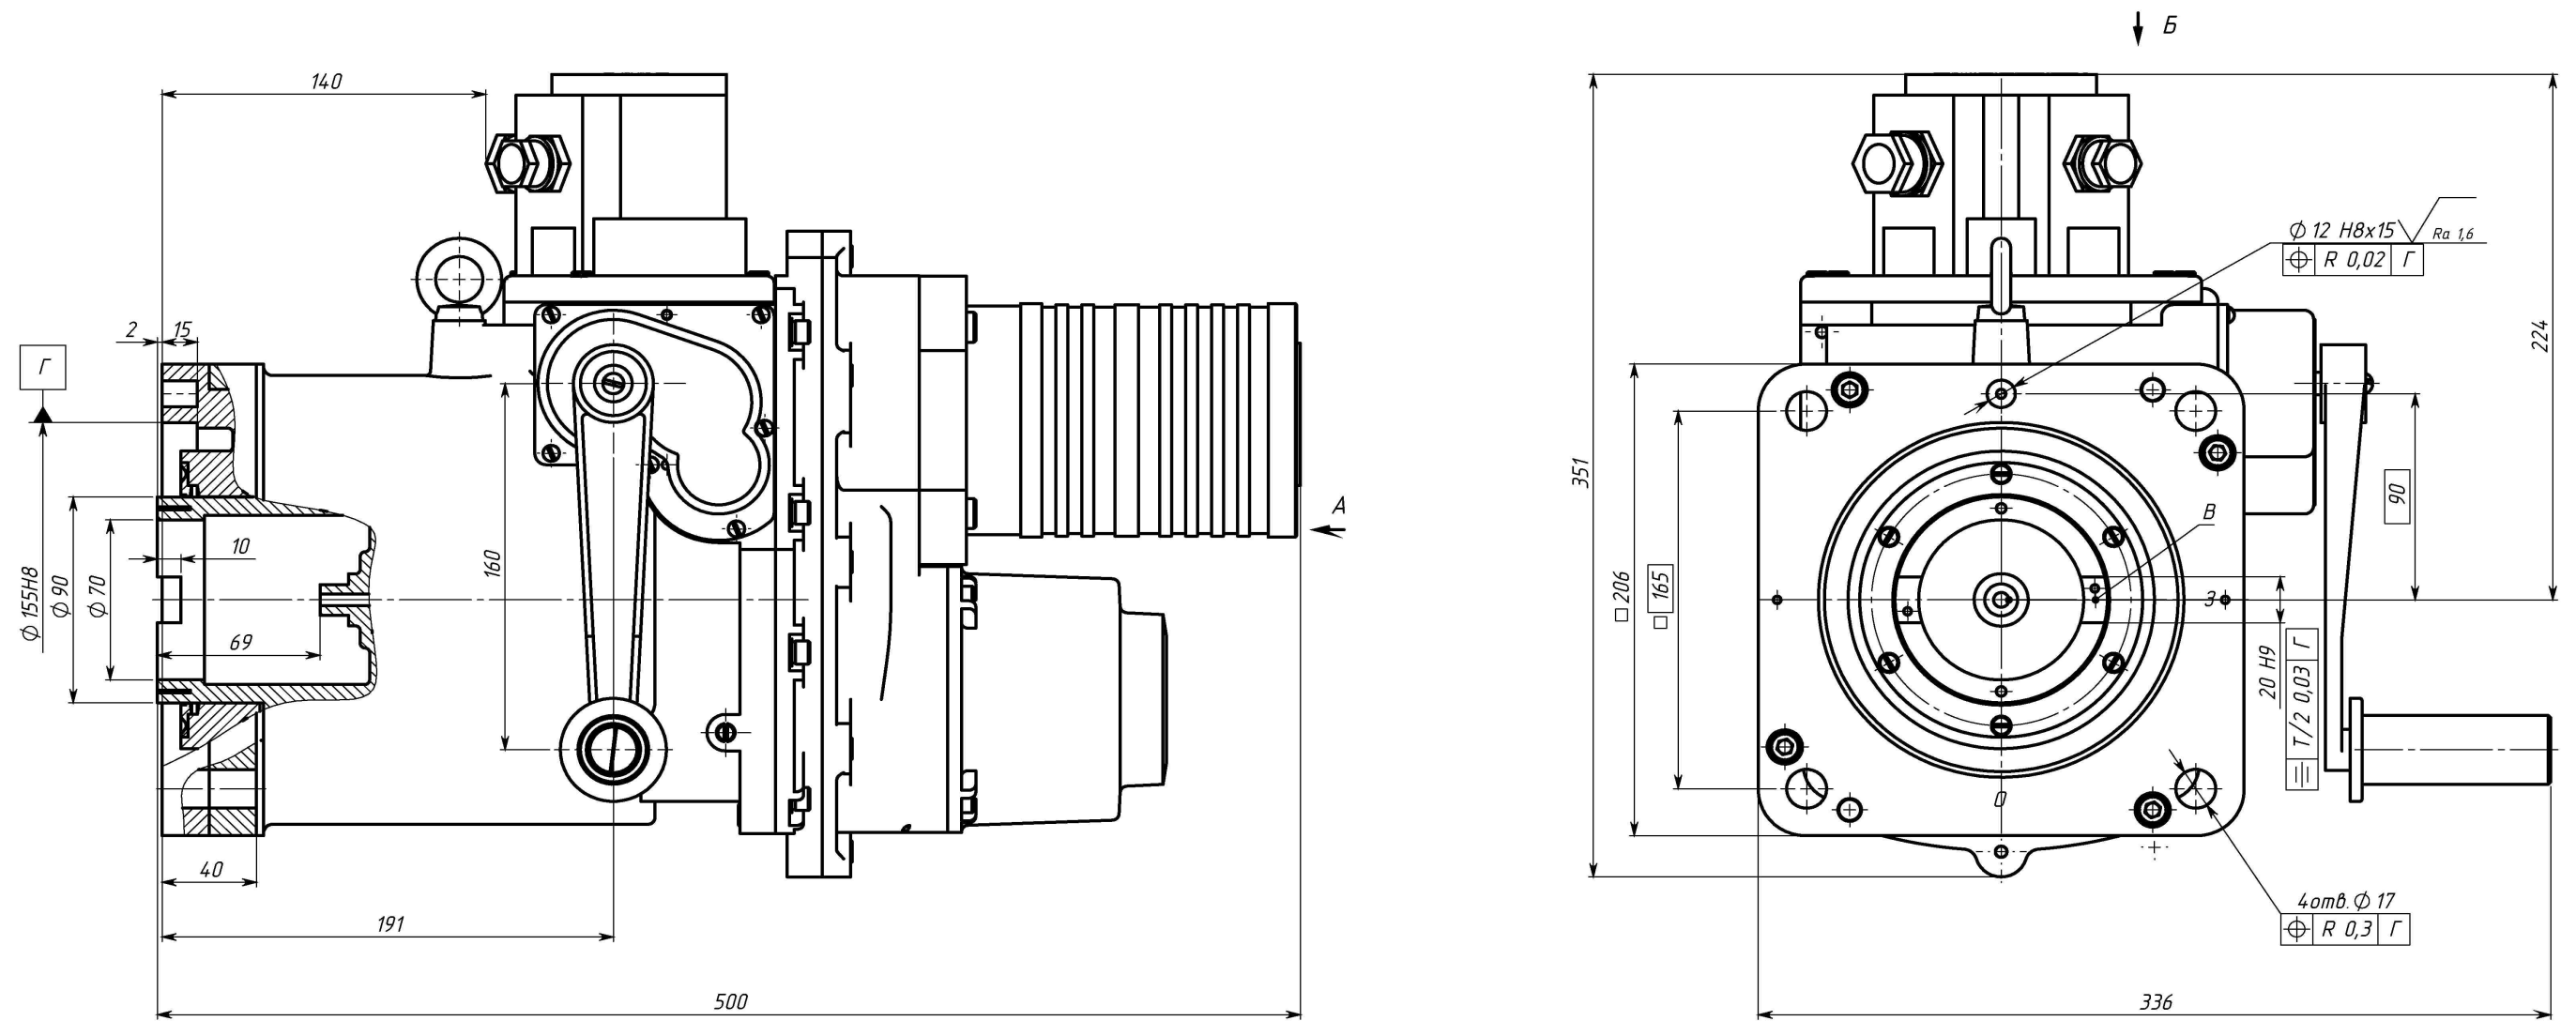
Габаритный чертеж механизмов М30ВУ-(500-1600)
